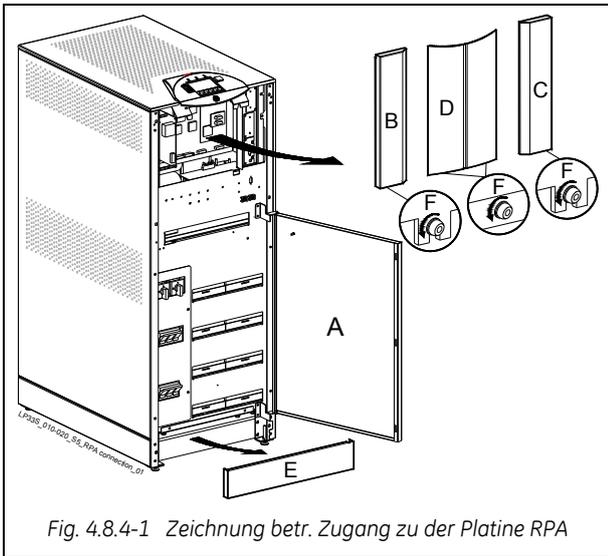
Zeichnung betr. Zugang zu der Platine RPA
